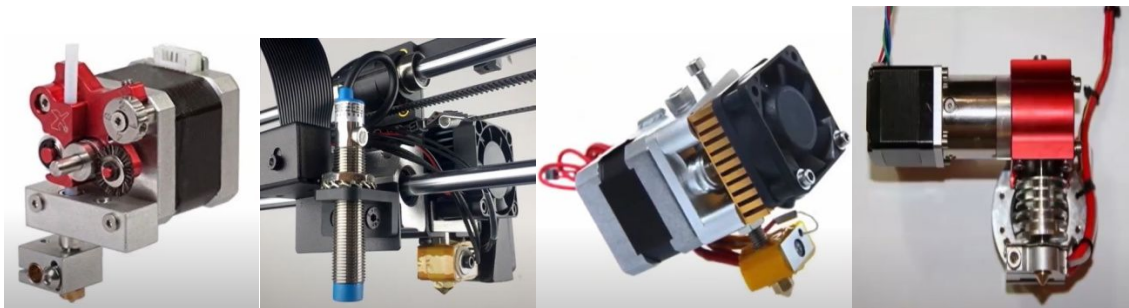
Внешний вид различных вариантов конструкций экструдеров
